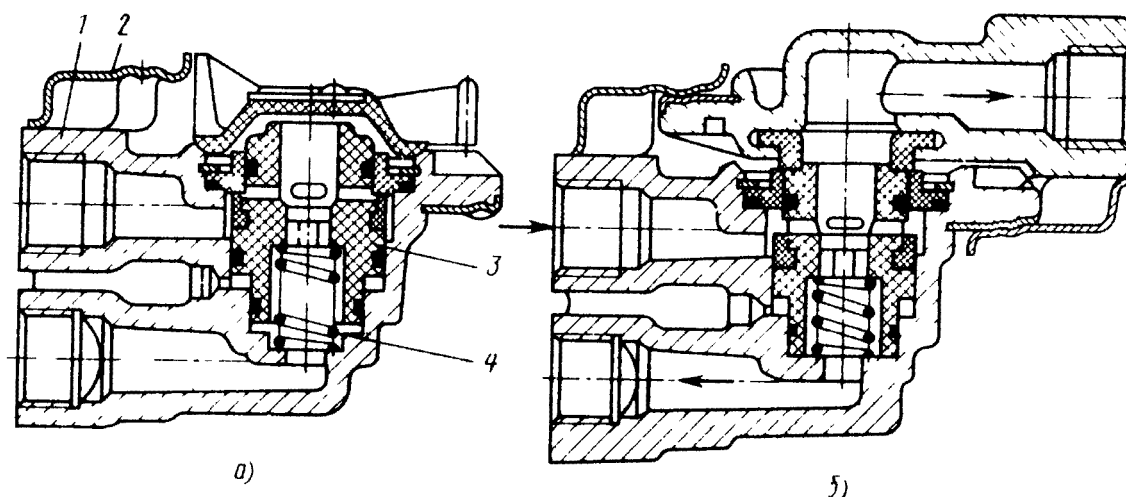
Соединительная автоматическая головка и соединение автоматической головки с головкой типа "Палм":
